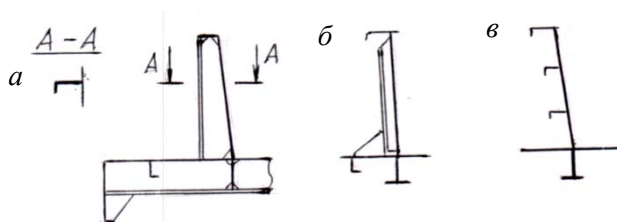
Конструкция ограждения грузовой палубы судов – площадок:
